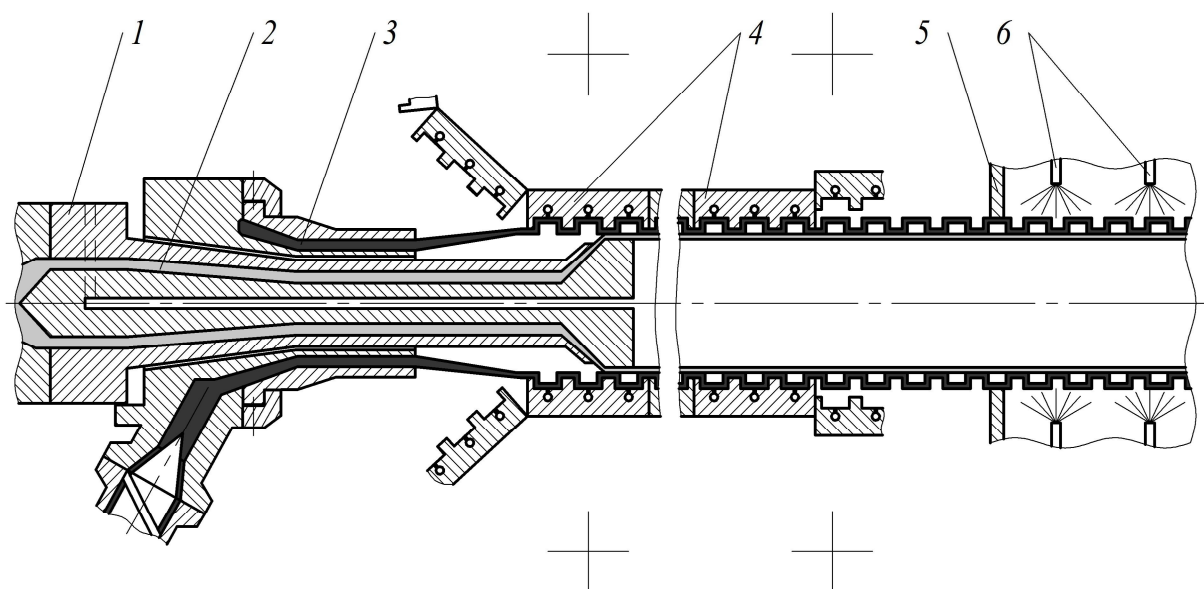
Схема виготовлення двошарових гофрованих труб: 1 – прямоточна екструзійна головка; 2 – кутова екструзійна головка; 3 – труба заготованка зовнішнього шару; 4 – півформи гофратора; 5 – ванна охолодження; 6 – форсунки
